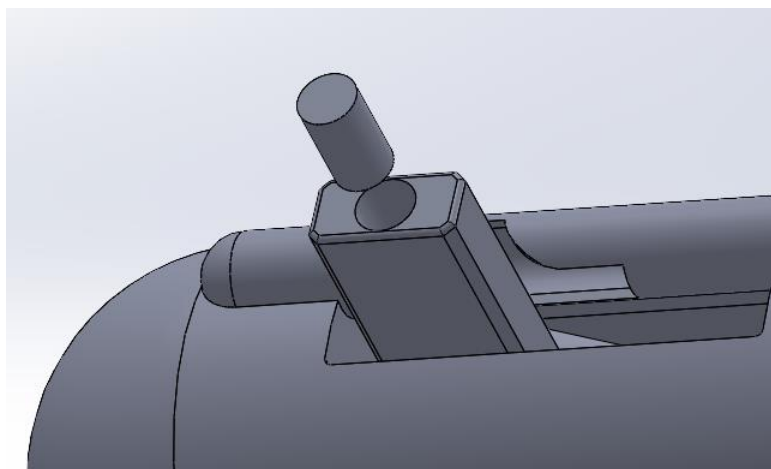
Quinta imagen de montaje, inserción del embellecedor del Gatillo.
